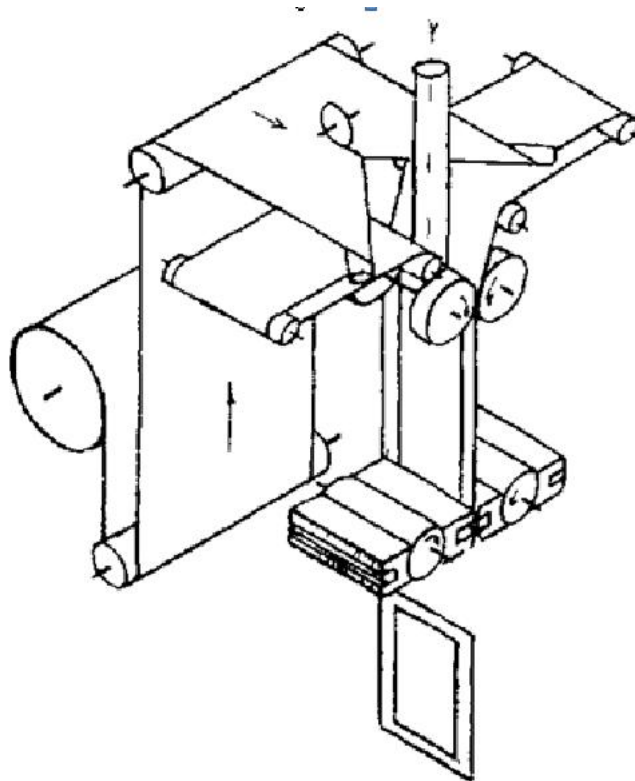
Схема машини для виготовлення чотирьох шовного пакету
